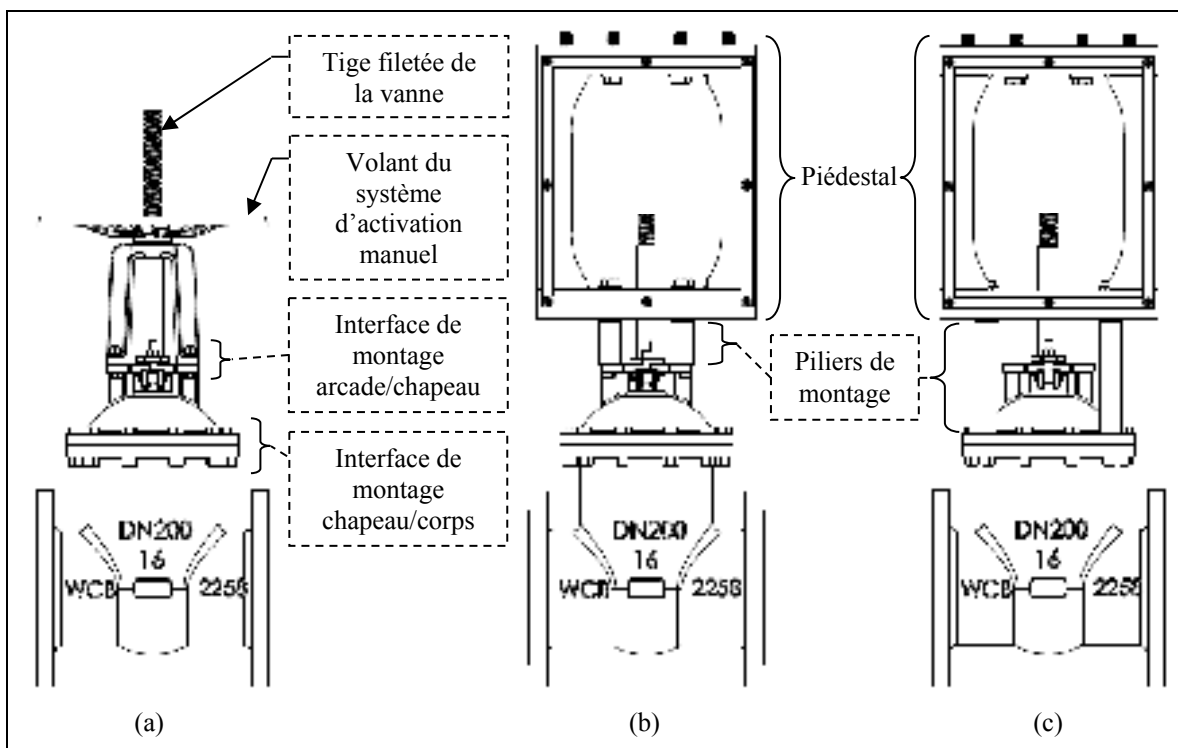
Éléments d'une vanne (a) et montage des piliers aux interfaces arcade/chapeau (b) et chapeau/corps (b)
